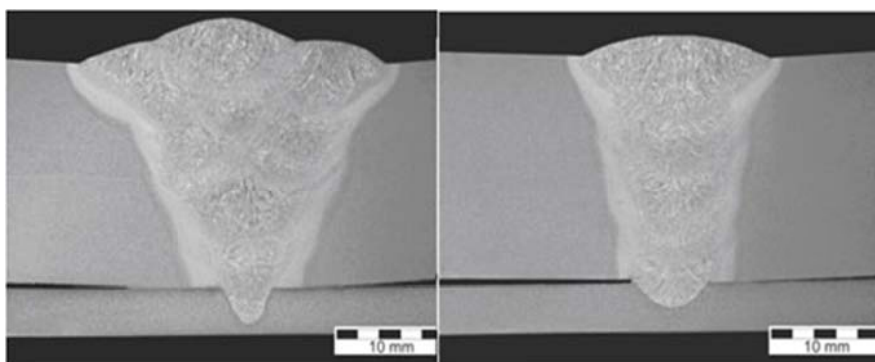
Микроструктура сварного соединения, полученного ручной дуговой сваркой
